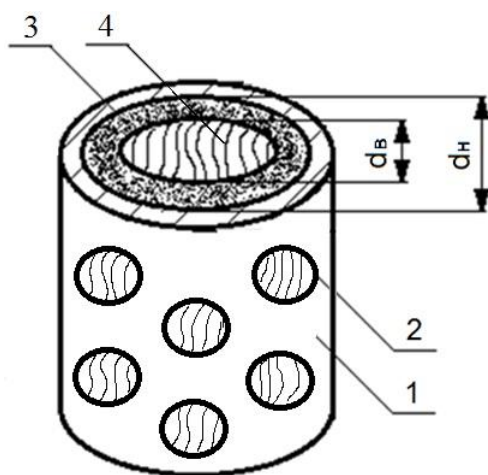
Схема конструкции поропластовой насадки (кольцо Рашига) [4]:
